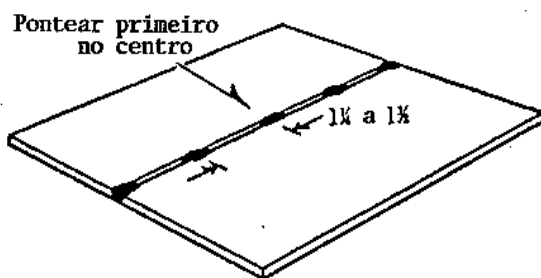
Método de soldagem de chapas de aço inoxidável.
